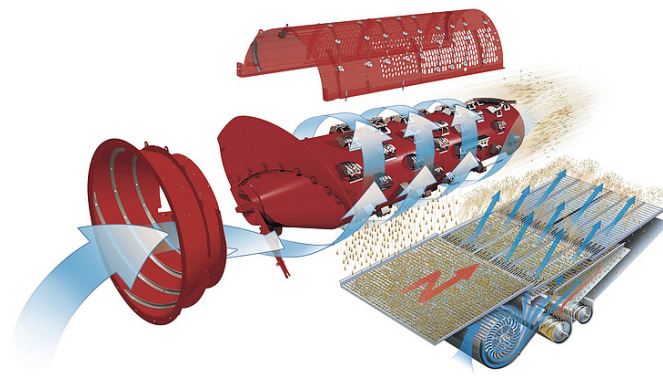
New Holland CR 9090 ELEVATION pohľad v reze.
